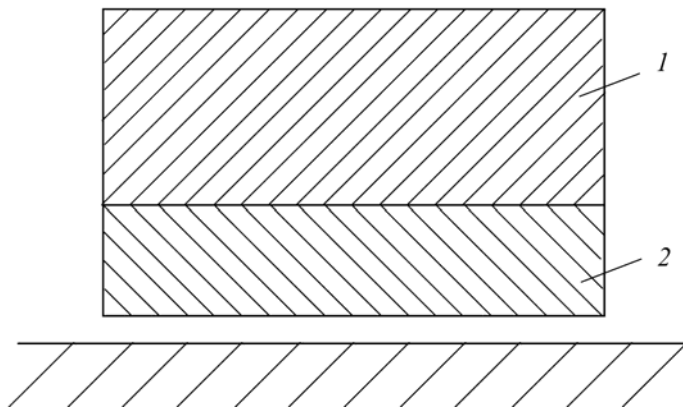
Конструкция подшипника скольжения со сплошной заливкой рабочей поверхности: 1 – сталь; 2 – оловянно-свинцовый сплав
